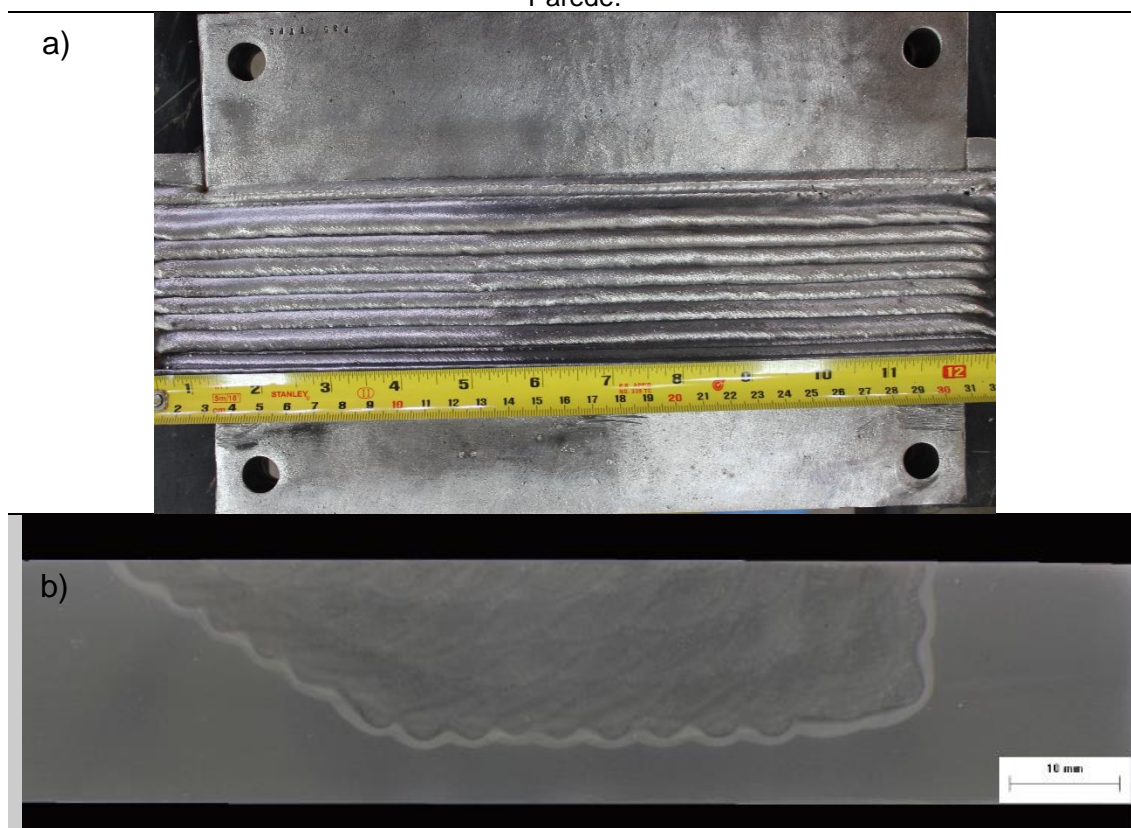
Reparo de parede – Corpo de prova soldado.
